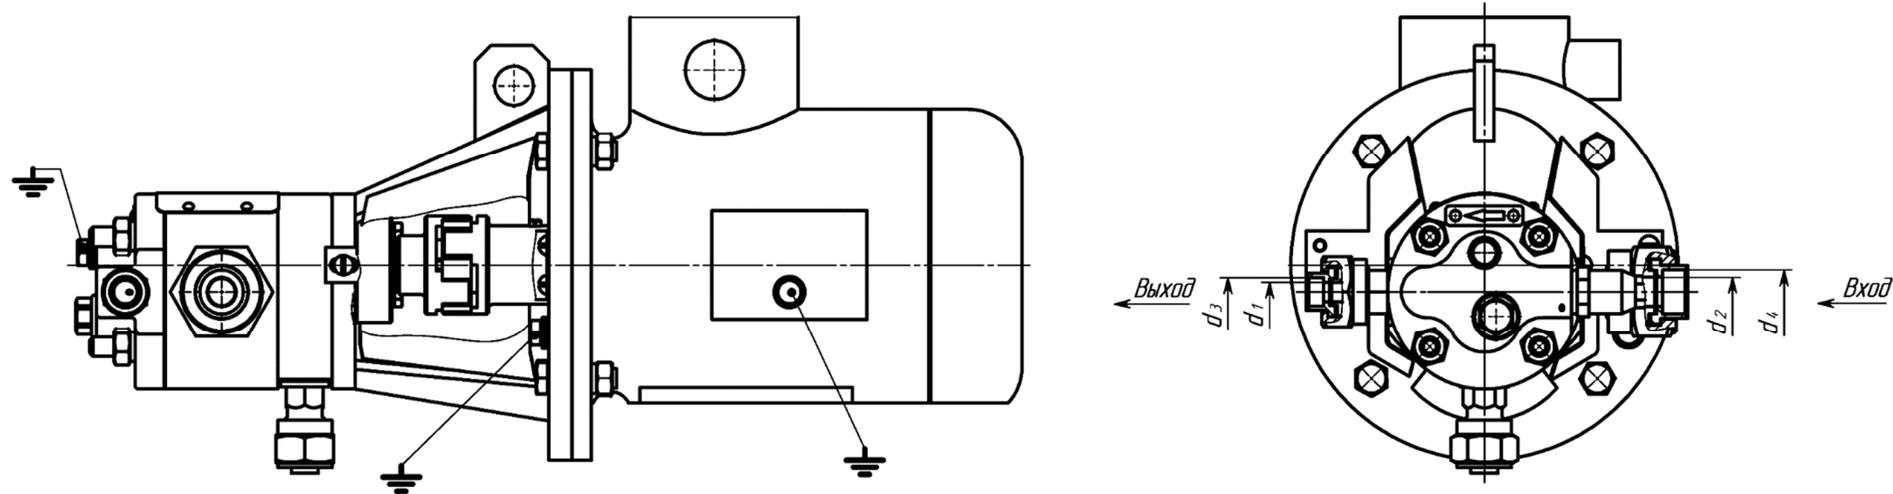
Габаритный чертеж агрегата типа НМШФ с правым вращением ведущего ротора.
